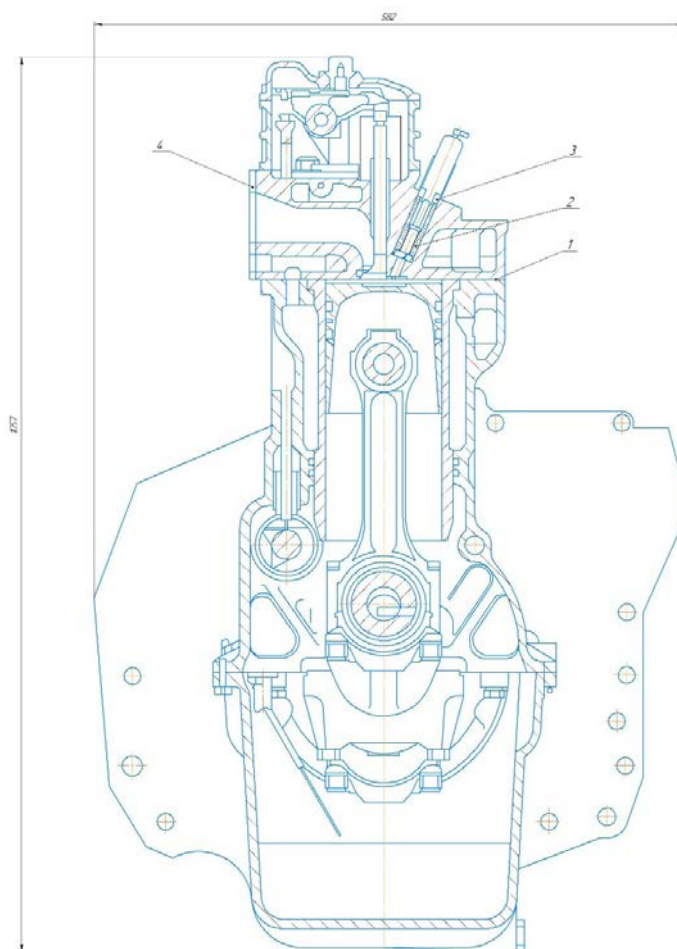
Поперечный разрез переподжатого газового двигателя:
